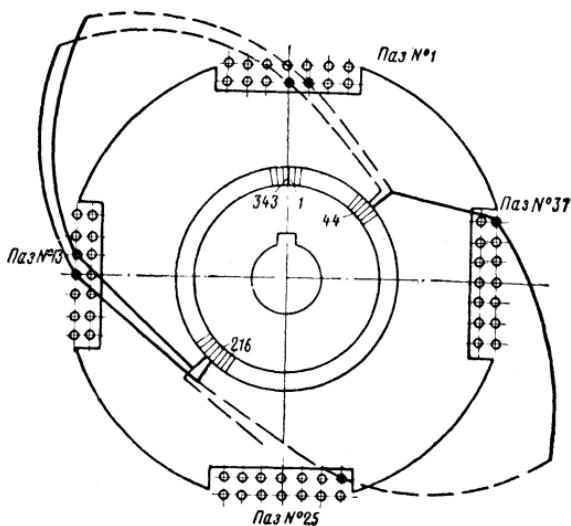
Схема соединения обмотки якоря двигателя НБ-431А с коллекторными пластинами
